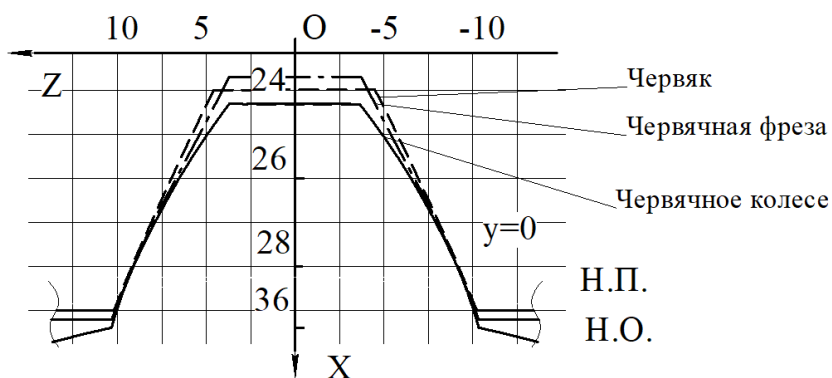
Профили червяка, червячной фрезы и червячного колеса в сечении $y=0$
